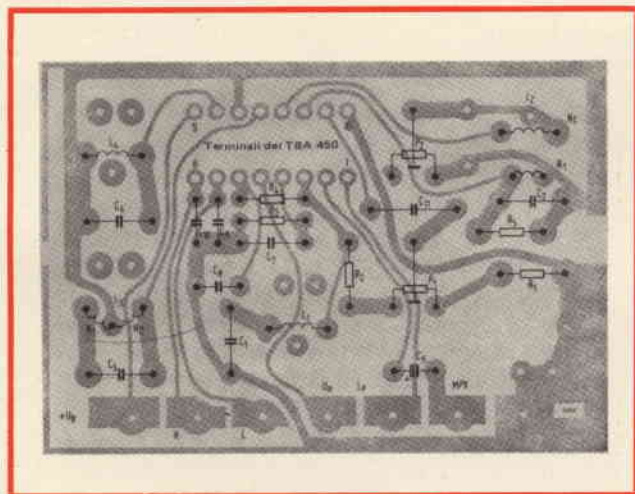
Circuito stampato del decoder stereo, visto dal lato saldature, con i componenti già montati.
